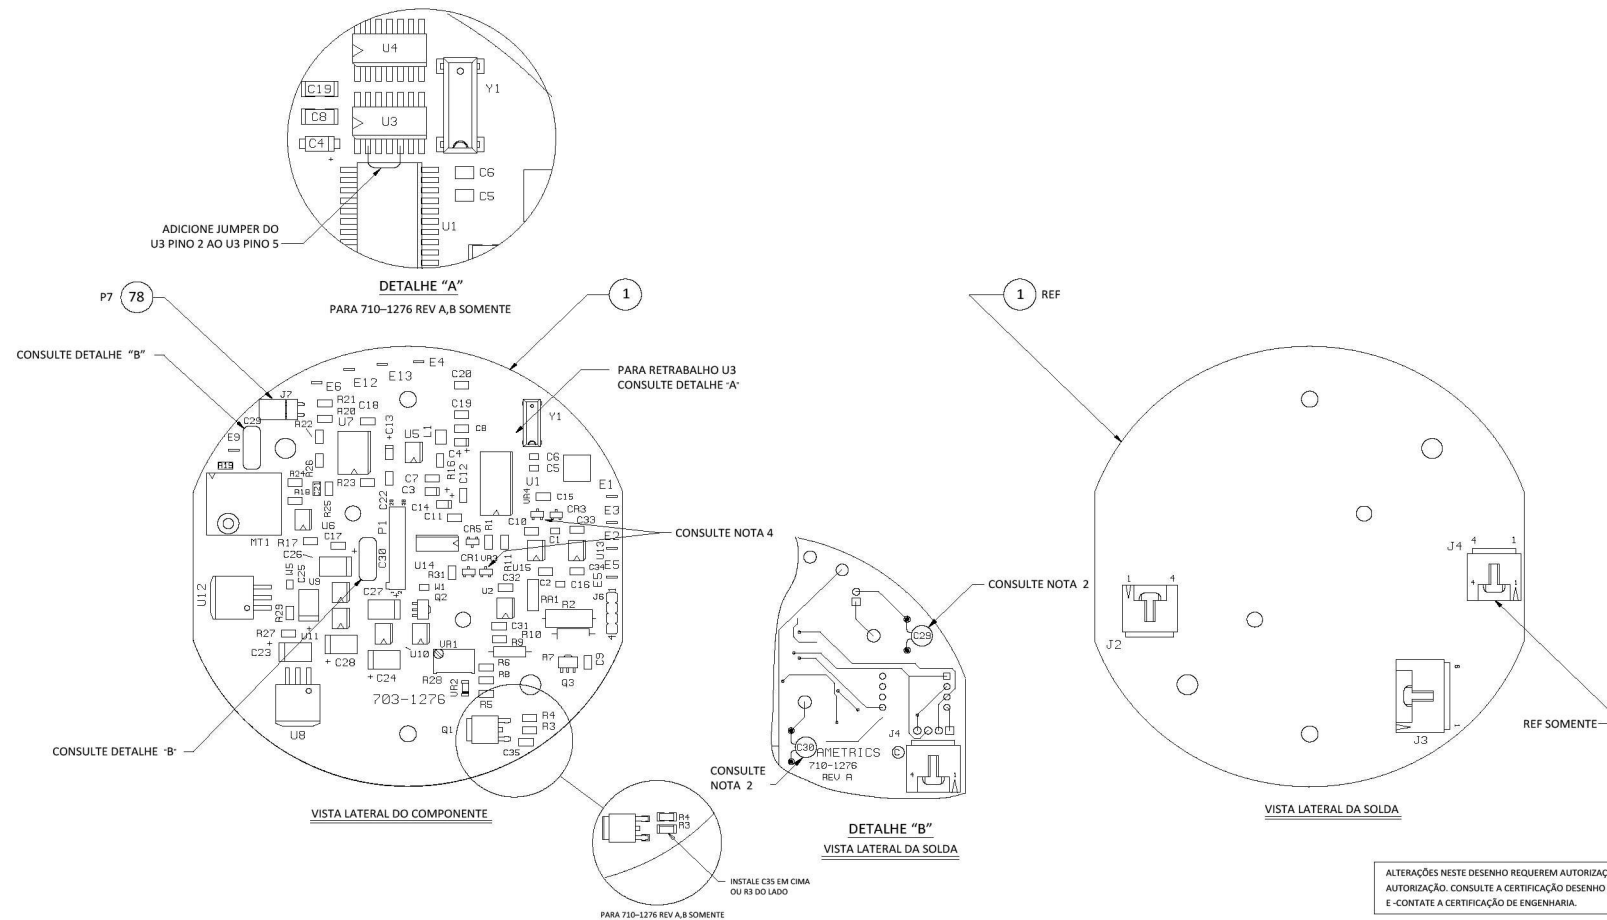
Esquema Digital de PCB (ref. 700-1316, rev. H, SH2)
